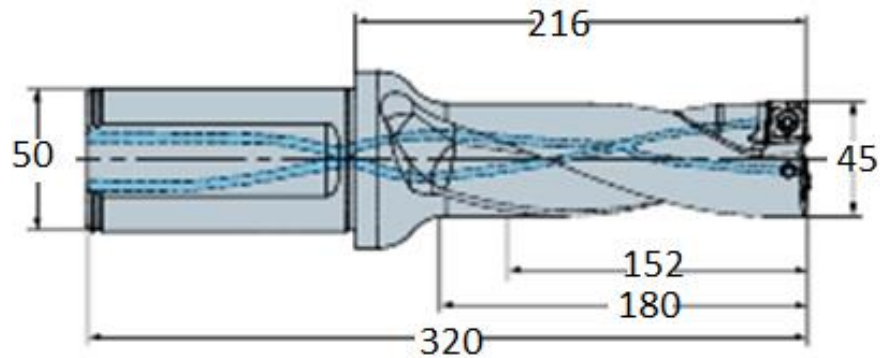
сверло Sandvik Coromant CoreDrill 880-D4500L50-04
